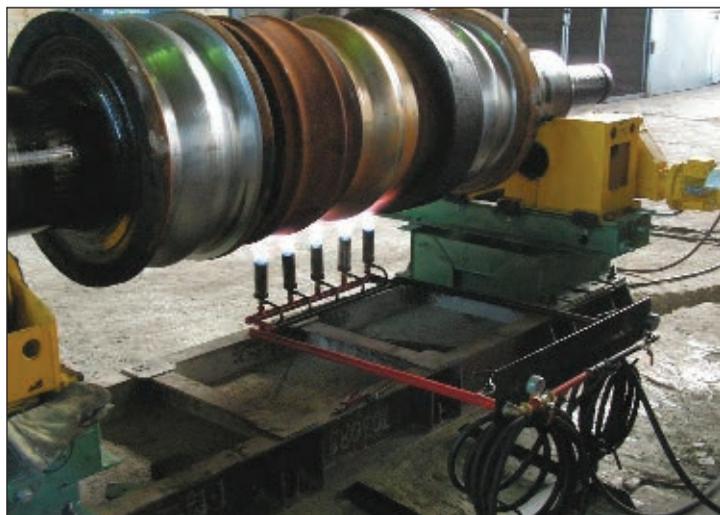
Установка для нагрева прокатных валков перед их наплавкой
